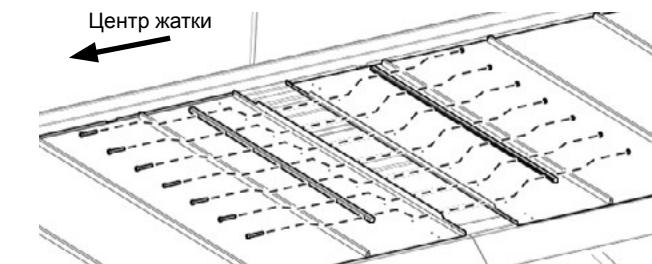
Установка соединительного стержня полотенного транспортера.
